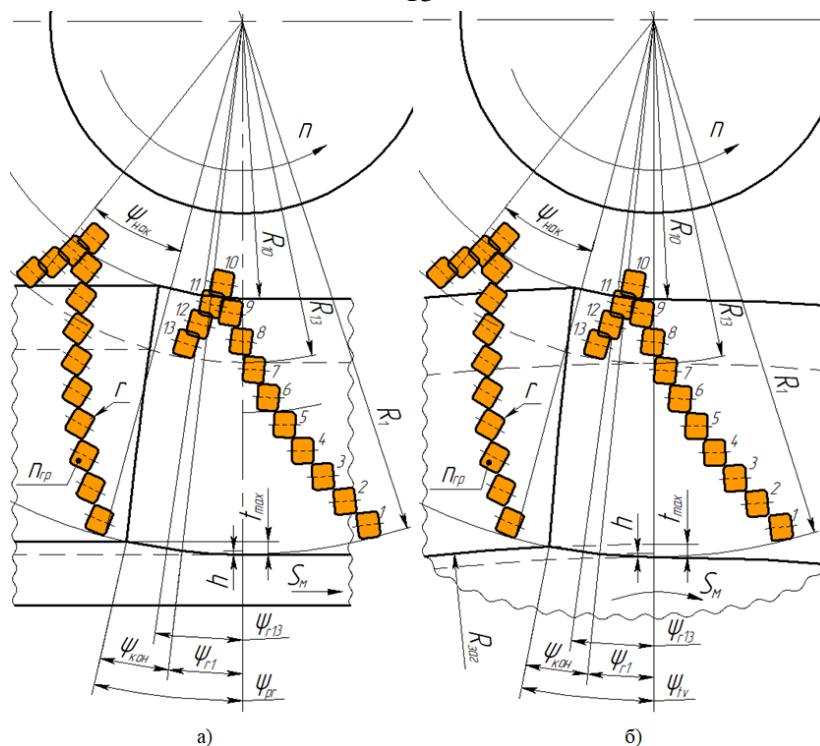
Схема попутного фрезерования: профиля головки рельсов (а), бандажа колесных пар (б)
